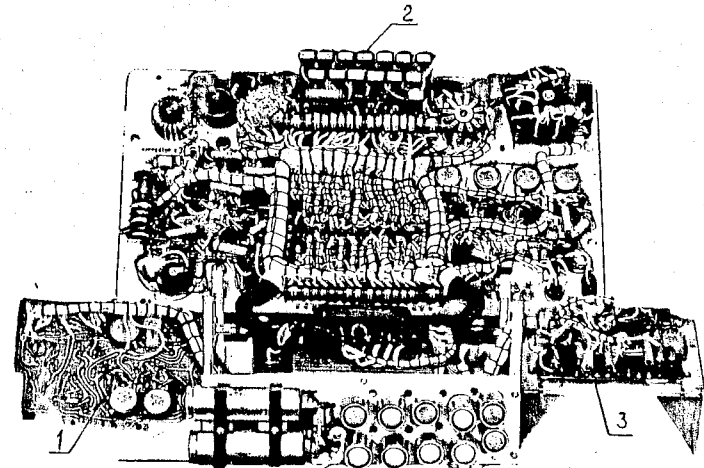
Gesamtansicht des Gerätes mit abgenom-
